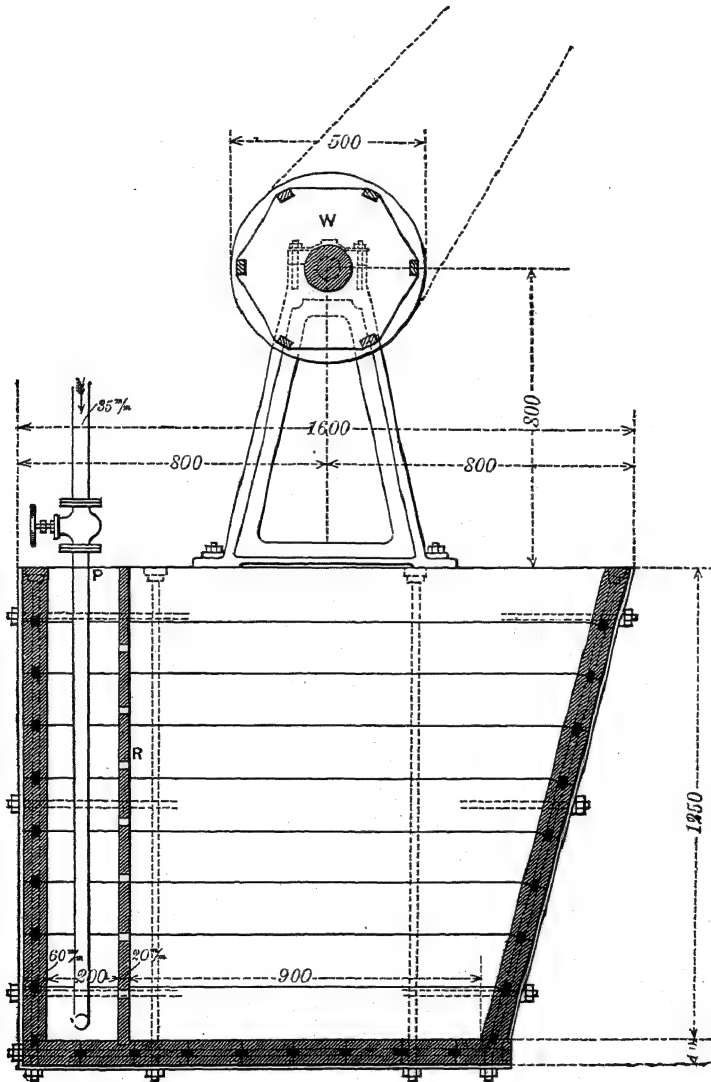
Stückfärbekufe mit Maschinenhaspel (Querschnitt von vorn).
